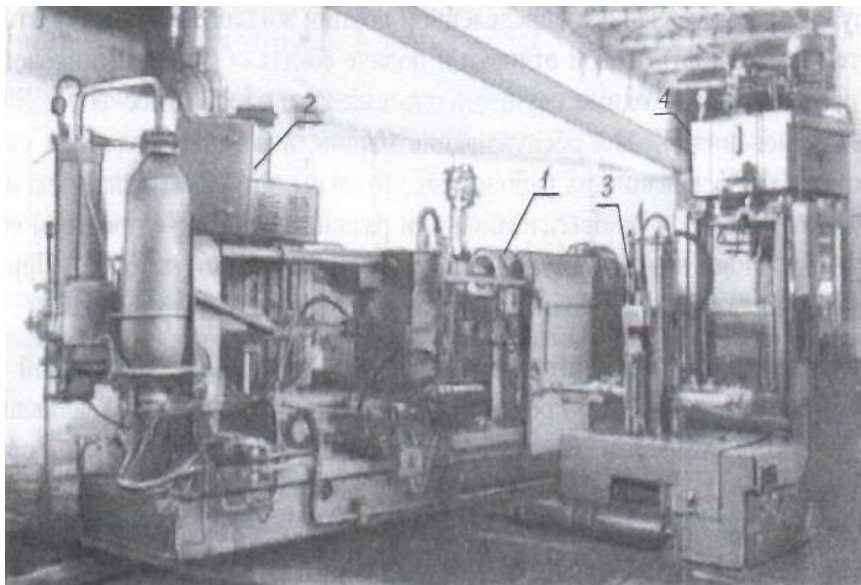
Роботизированный комплекс литья под давлением (вид со стороны робота, снимающего отливку) [4]:
